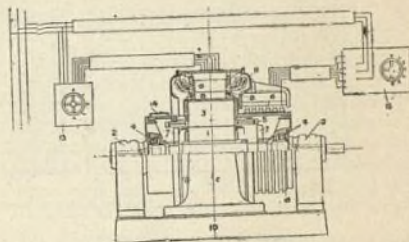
Motor trifásico.—Grupo conectado directamente.
